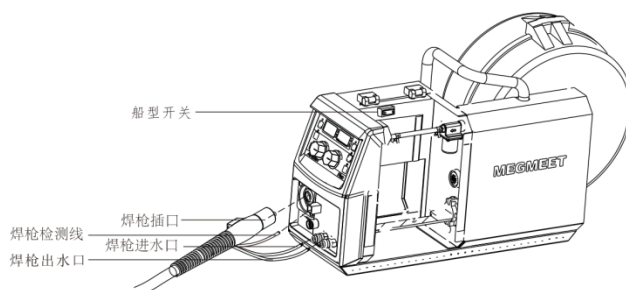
封闭式手工送丝机焊枪连接示意图
